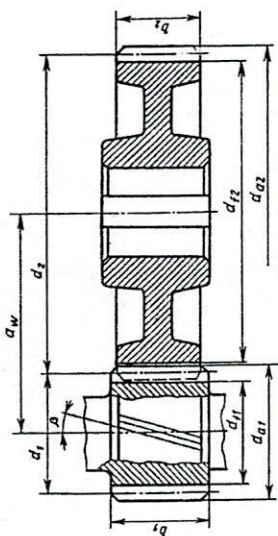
Геометрические параметры цилиндрической зубчатой передачи
